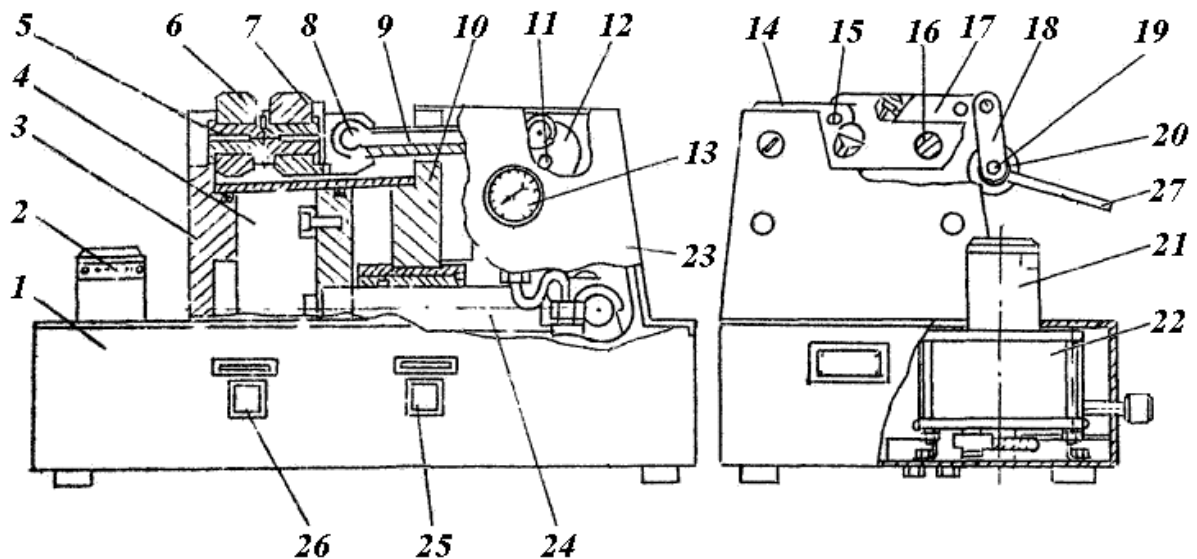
Конструктивная схема машины МСХС-5-3: 1 – корпус; 2 – сменная планка; 3 – крышка пневмоцилиндра; 4 – пневмоцилиндр; 5 – зажимные губки; 6 – неподвижный зажим; 7 – подвижный зажим; 8 – ось; 9 – тяга; 10 – крышка пневмоцилиндра; 11 – ось; 12 – рычаг; 13 – манометр; 14 – основание зажима; 15 – ось; 16 – направляющая; 17 – рычаг; 18 – тяга; 19 – ось; 20 – эксцентрик; 21 – механизм обрезки; 22 – пневмоцилиндр; 23 – кожух; 24 – шток; 25 – кран механизма осадки; 26 – кран механизма обрезки; 27 – рукоятка эксцентрика
